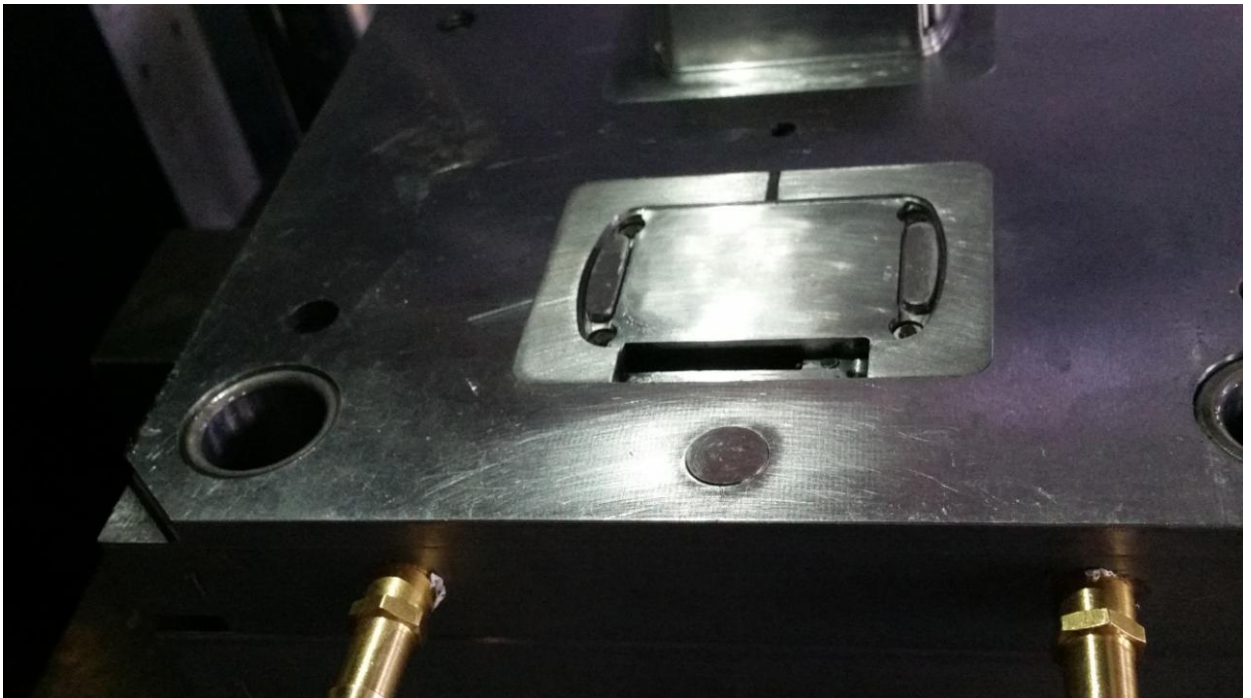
Изготовленные ложементы пресс – формы с использованием фрезерного обрабатывающего центра
